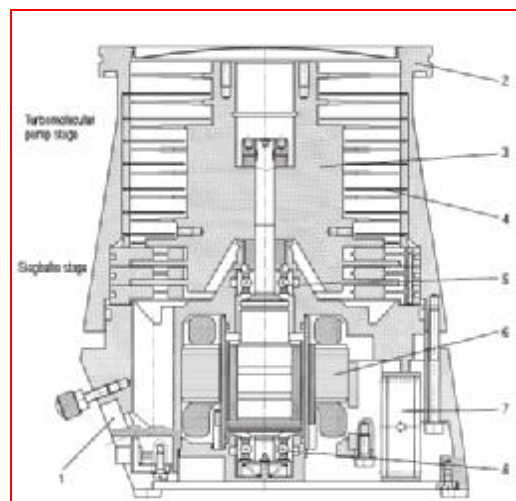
Турбомолекулярный насос TURBOVAC151 с обычными подшипниками со смазкой
